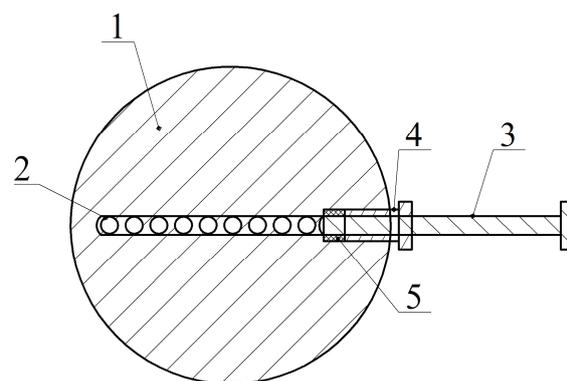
Регулируемая дроссельная шайба: 1 – корпус, 2 – проходные отверстия, 3 – регулировочный болт, 4 – сальниковый болт, 5 – сальниковая набивка
